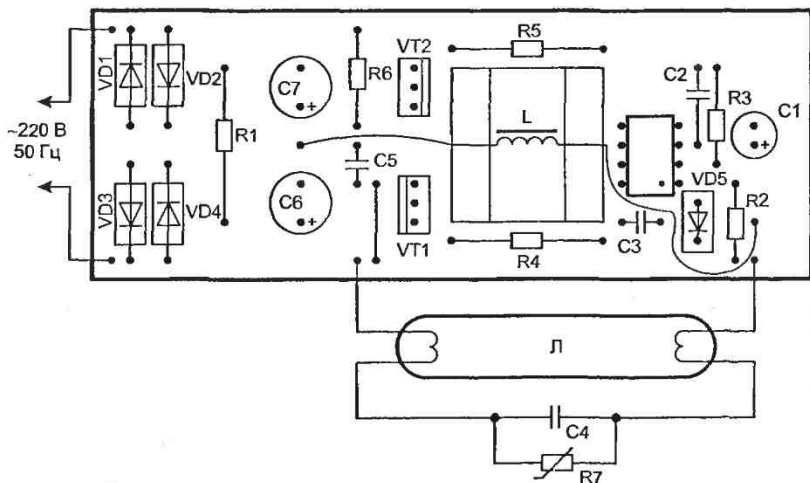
Сборочный чертеж платы экспериментального балласта
